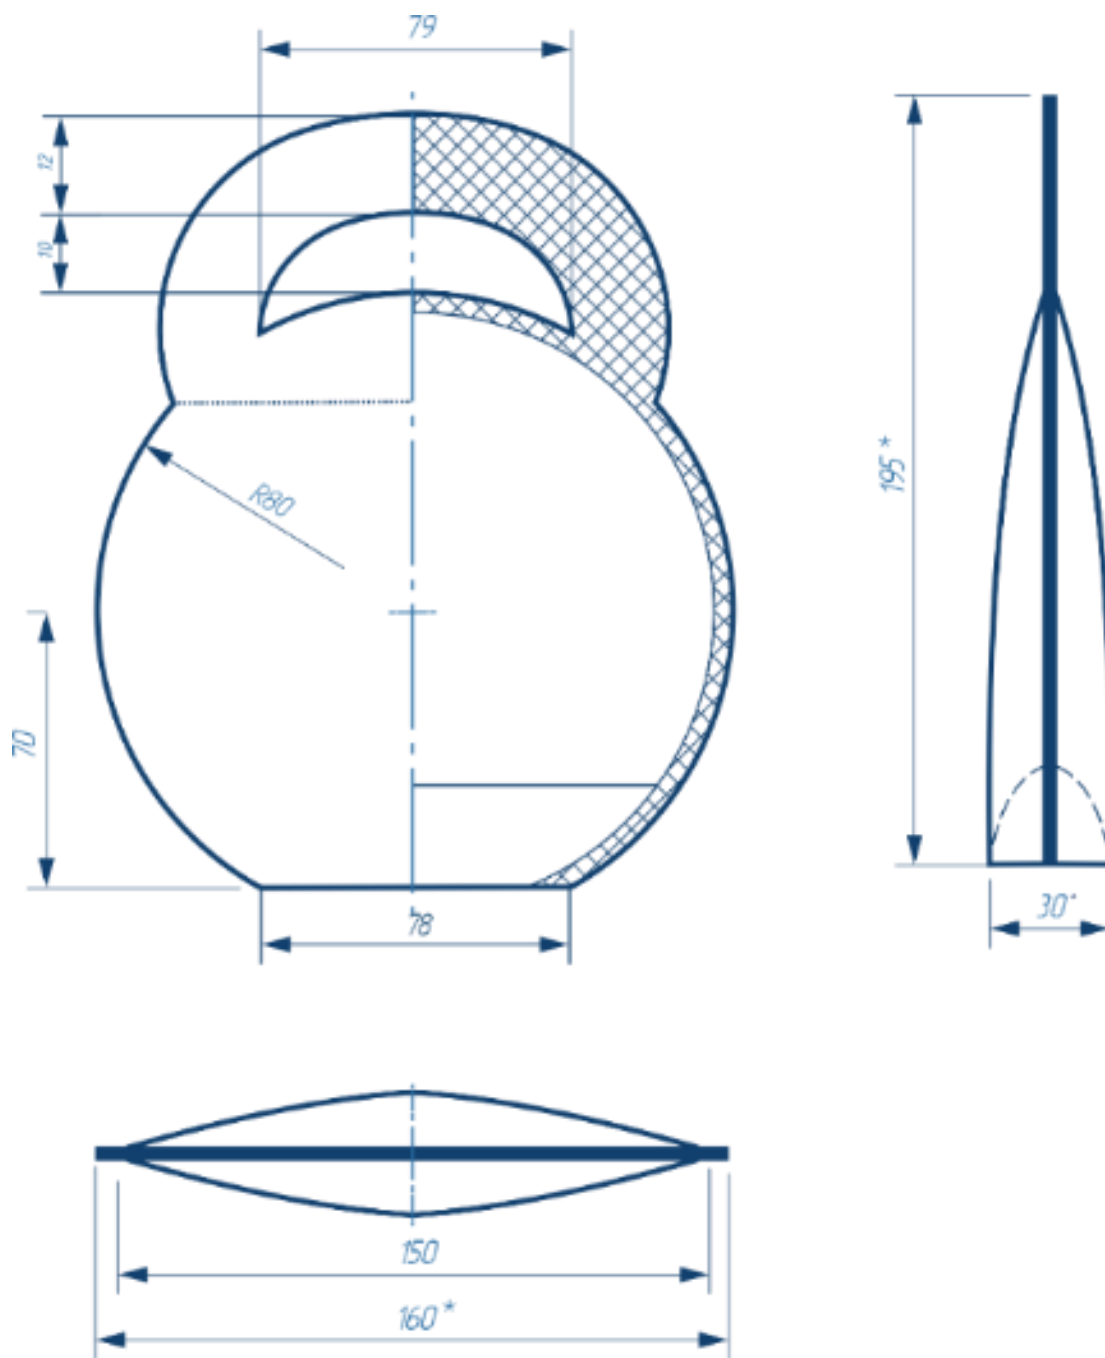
Изображение: а – развертки упаковки для фисташек;
